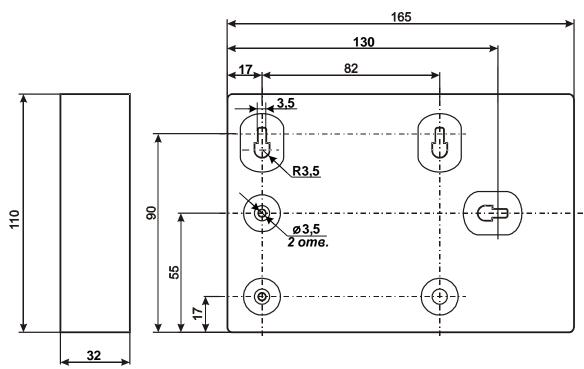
Габаритные и присоединительные размеры КД2 (исполнение IP20)
